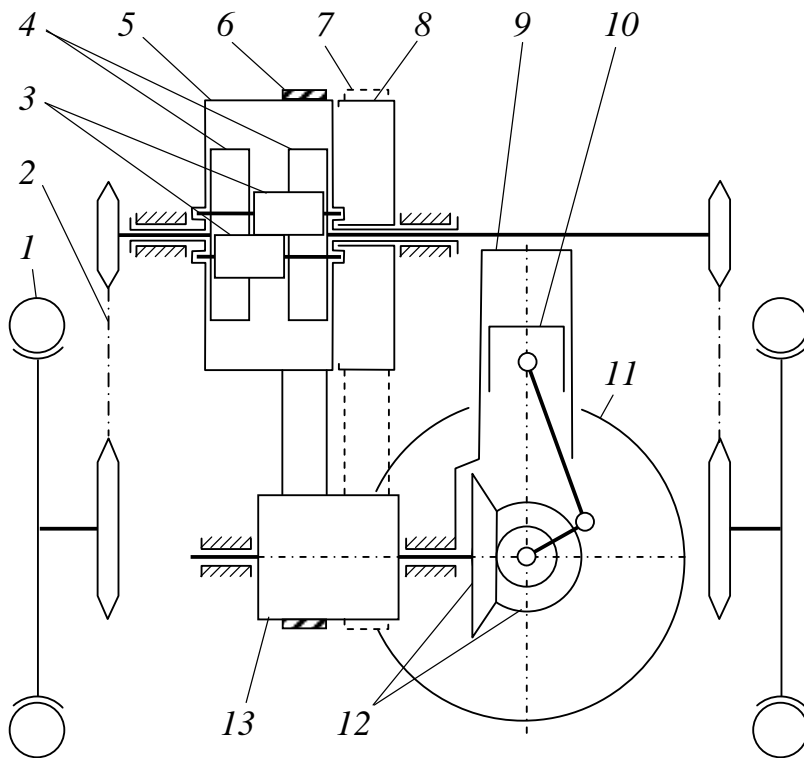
Трансмиссия автомобиля Бенца, 1885 г.: 1 – ведущее колесо автомобиля; 2 – цепь привода колеса; 3 – сдвоенные сателлиты; 4 – полуосевые шестерни; 5 – ведомый шкив ремённой передачи; 6 – ремень в положении «движение»; 7 – ремень в положении «холостой ход»; 8 – шкив холостого хода; 9 – цилиндр; 10 – поршень; 11 – маховик; 12 – коническая передача; 13 – ведущий шкив
